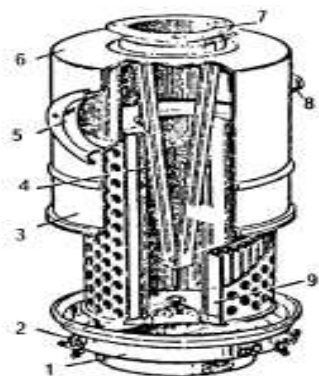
воздушный фильтр дизельного двигателя КамАЗ-740
